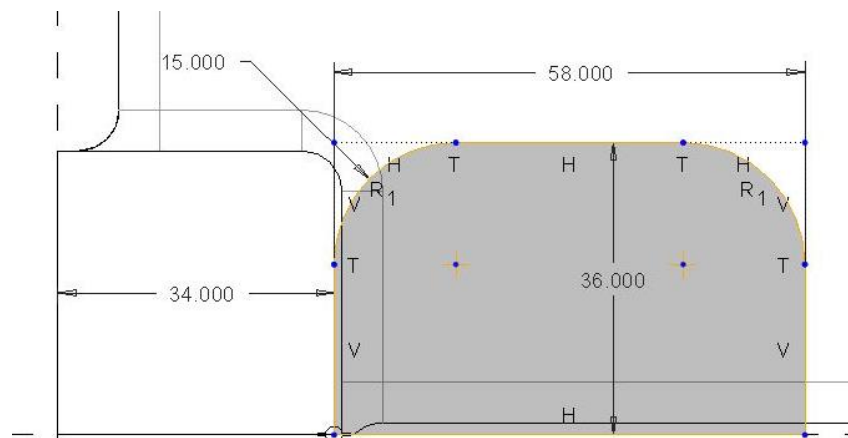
Skizze Planfläche Ölschauglas und Ölablassschraube
